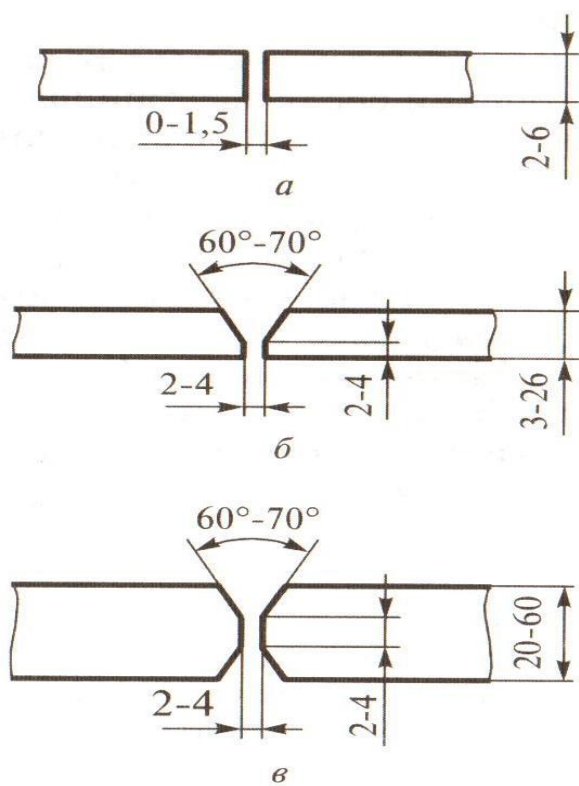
Способы подготовки кромок для стыковых соединений
